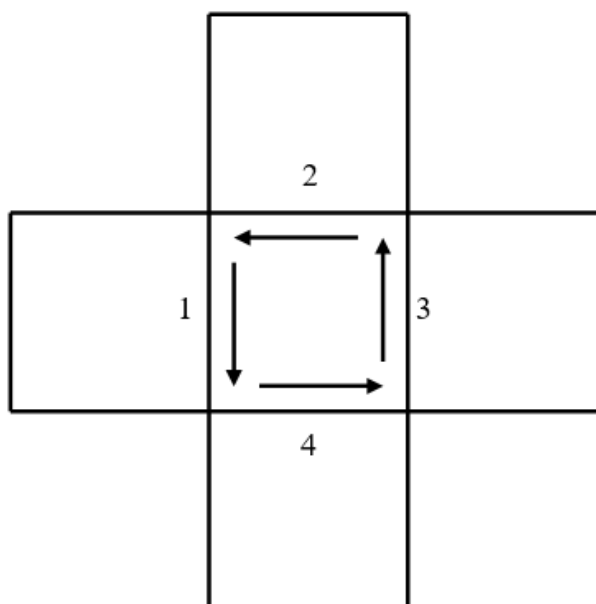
Схема сварки крестовой пробы.
